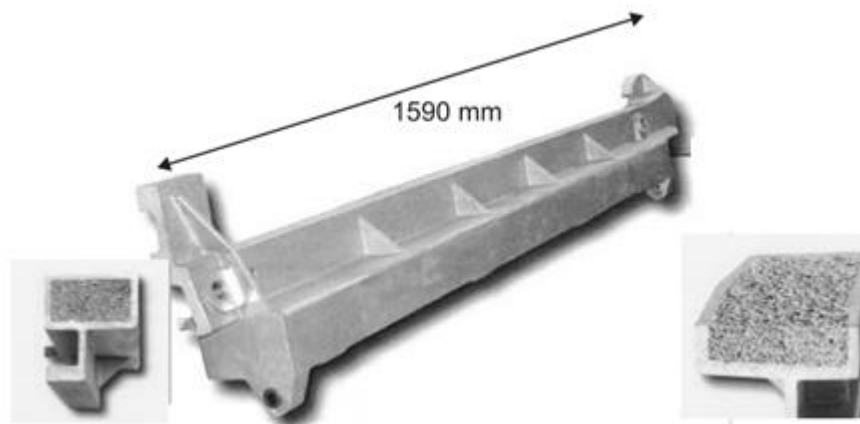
Suporte de fixação do motor de um protótipo BMW fabricado pela LKA.
